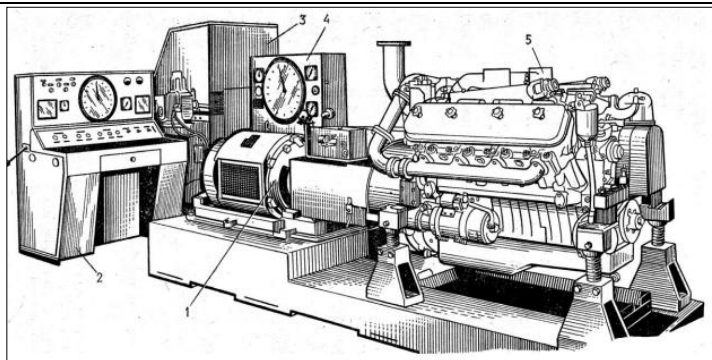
Стенд для обкатки двигунів КИ-1363Б:
